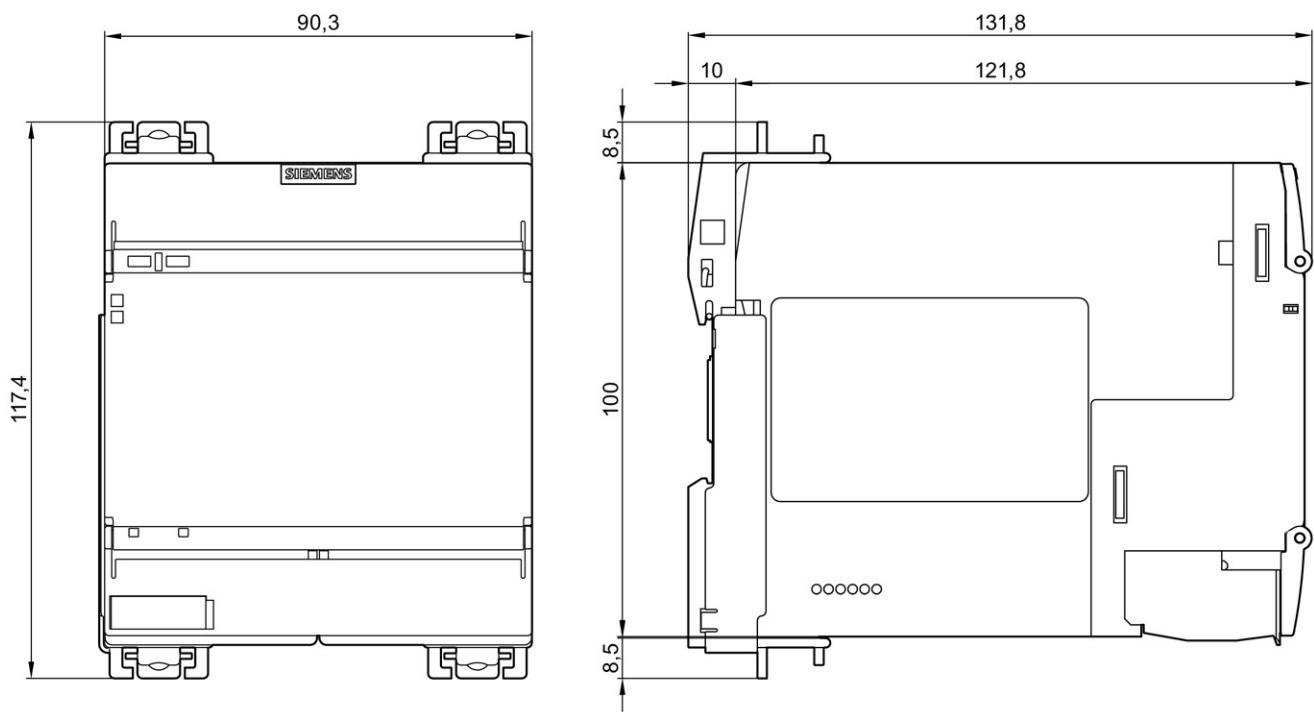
Gerät 3SK1213 auf Geräteverbinder
